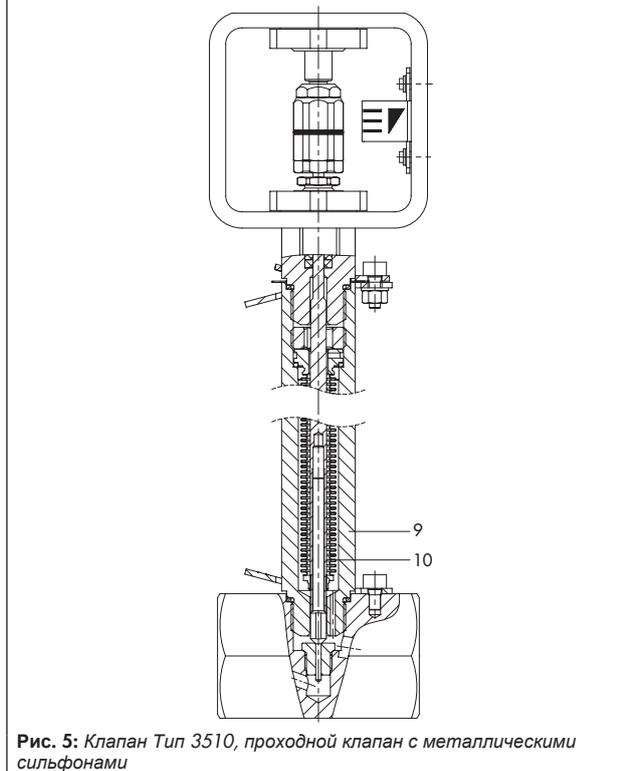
Клапан Тип 3510, проходной клапан с металлическими сальфонами
